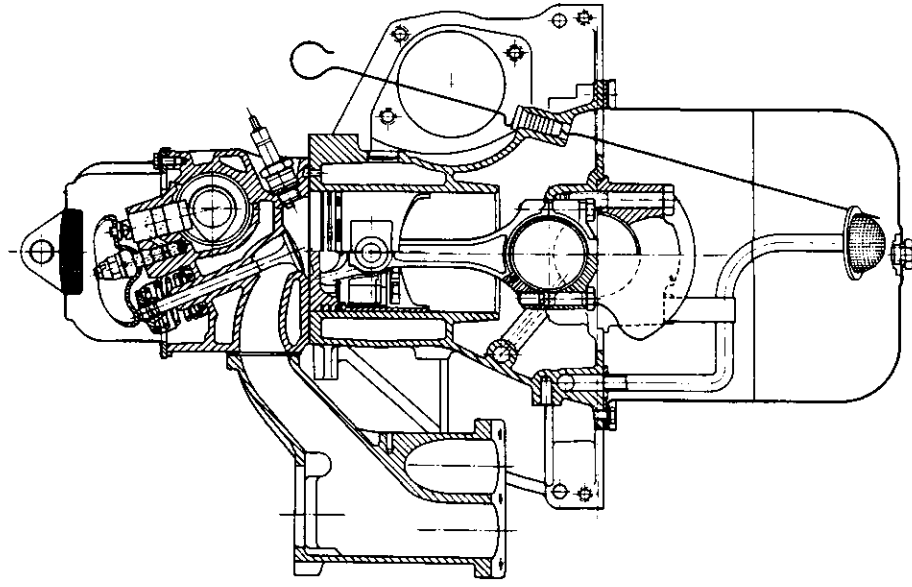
Ottomotor (Fa. Opel), Querschnitt
